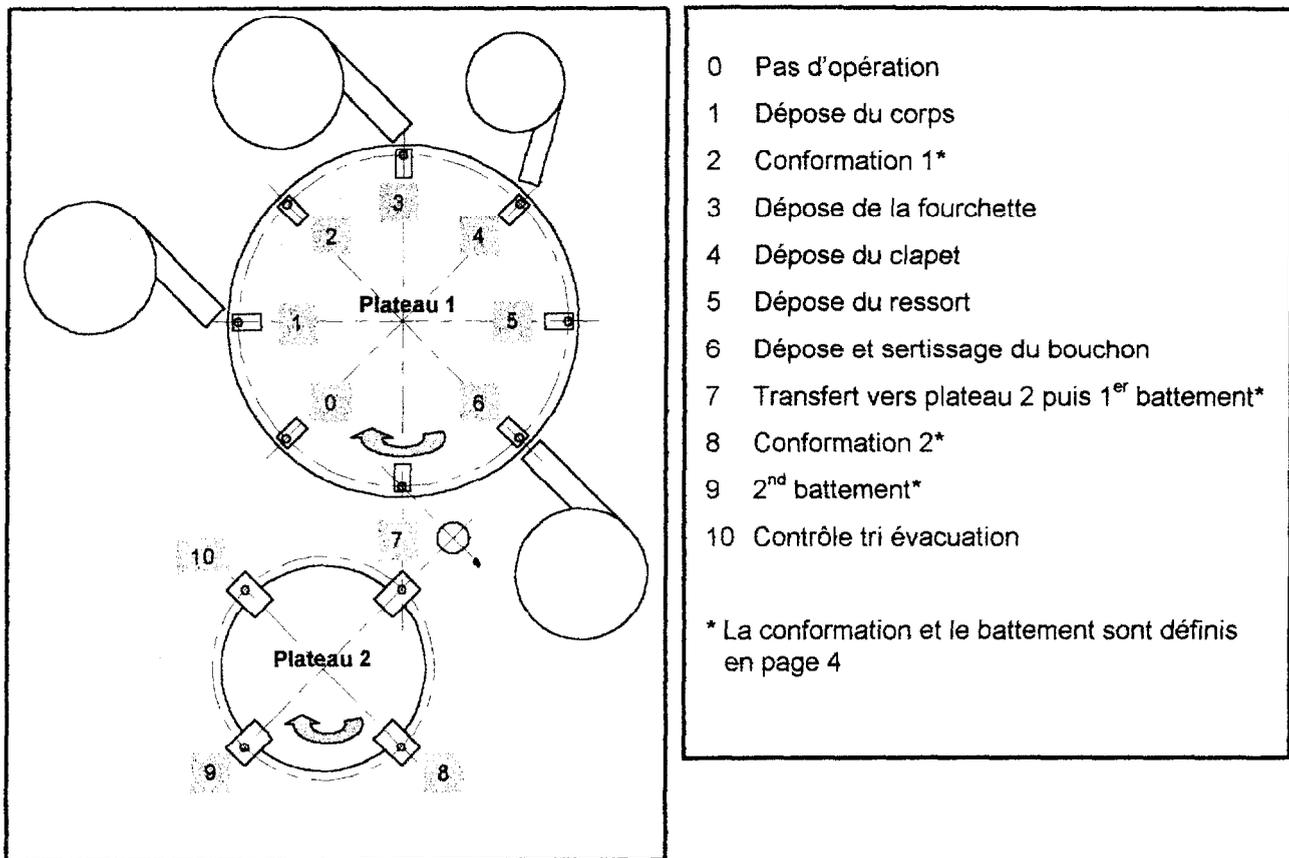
Architecture de la machine d'assemblage des cartouches pneumatiques.
